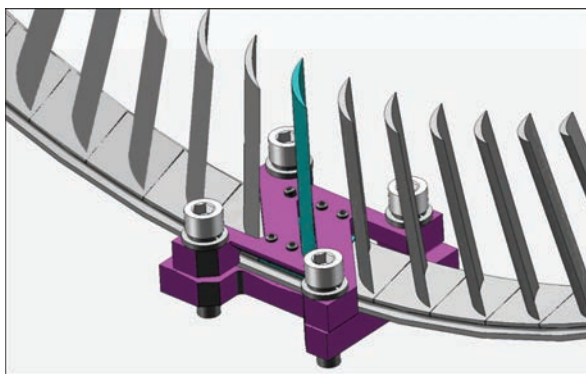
Модель сборочно-сварочного приспособления для ЭЛС консольной лопатки-донора с полуколысцом направляющего аппарата
